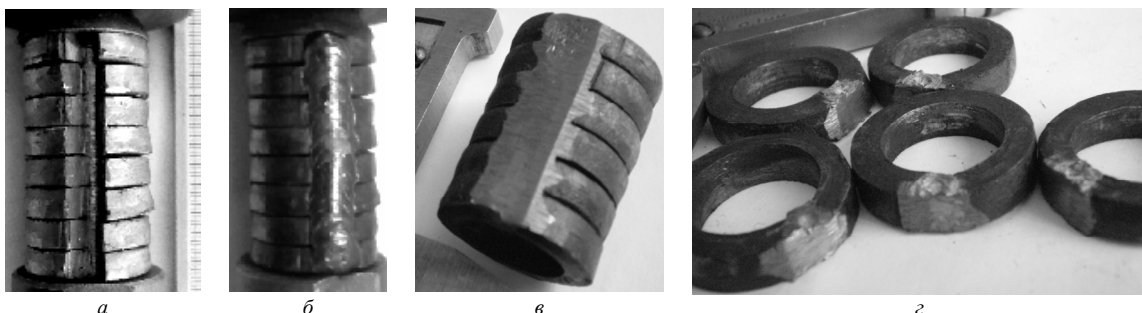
Пакет кілець до (а) і після (б) зварювання та зварна конструкція із зачищенням зварним швом (в) та відокремлені від неї крутильним моментом одиничні заготовки (г)
